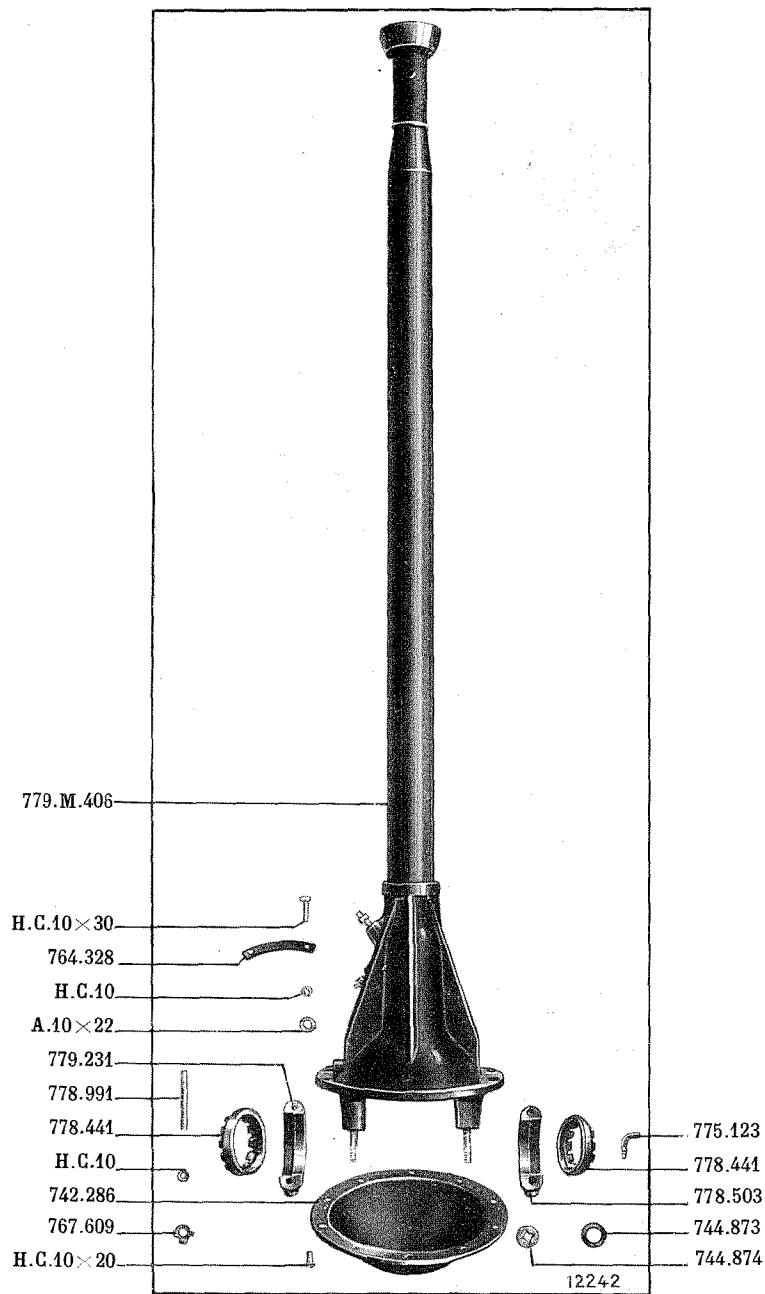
Couvercle et bouchons de l'essieu arrière.
